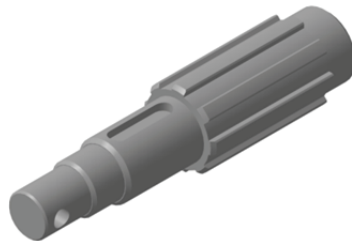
Прямой шлицевой цилиндрический вал сплошного сечения
